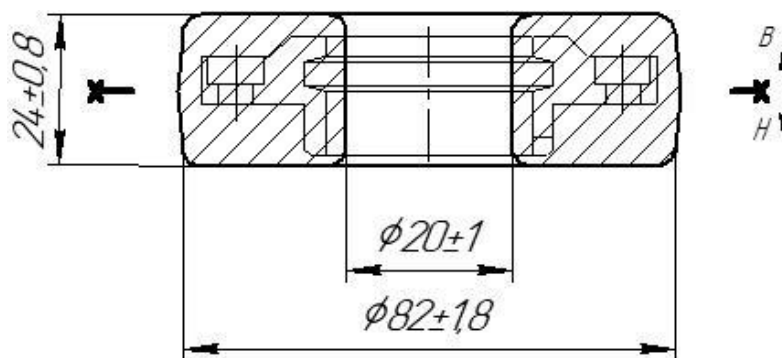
Ескіз первинної заготовки «Кришки підшипника»
